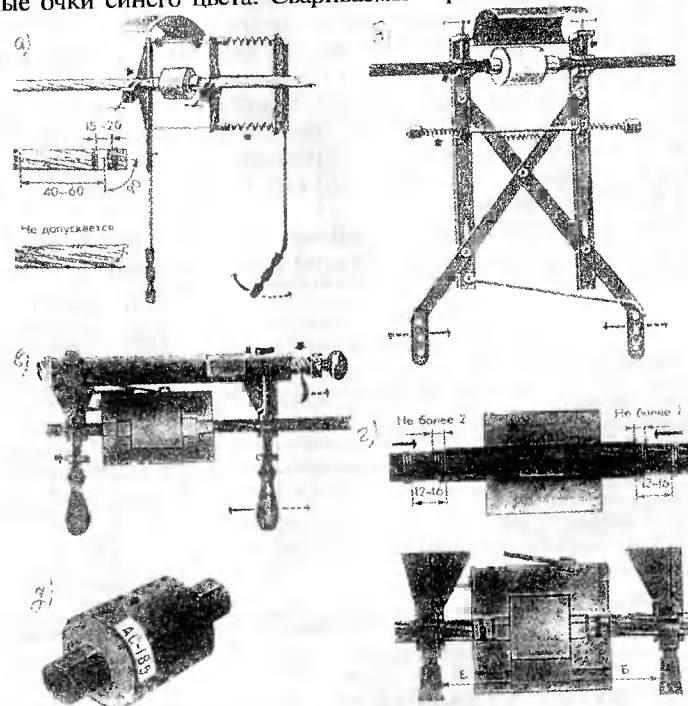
Приспособление для термитной сварки проводов (а, б, в); термитный патрон перед сваркой (г); термитный патрон АС-185 (д)
